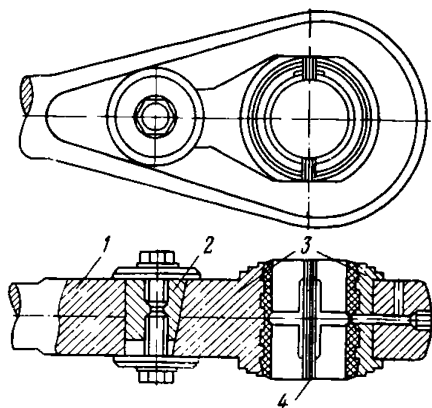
Крейцкопфный подшипник компрессора 2ВГ:
